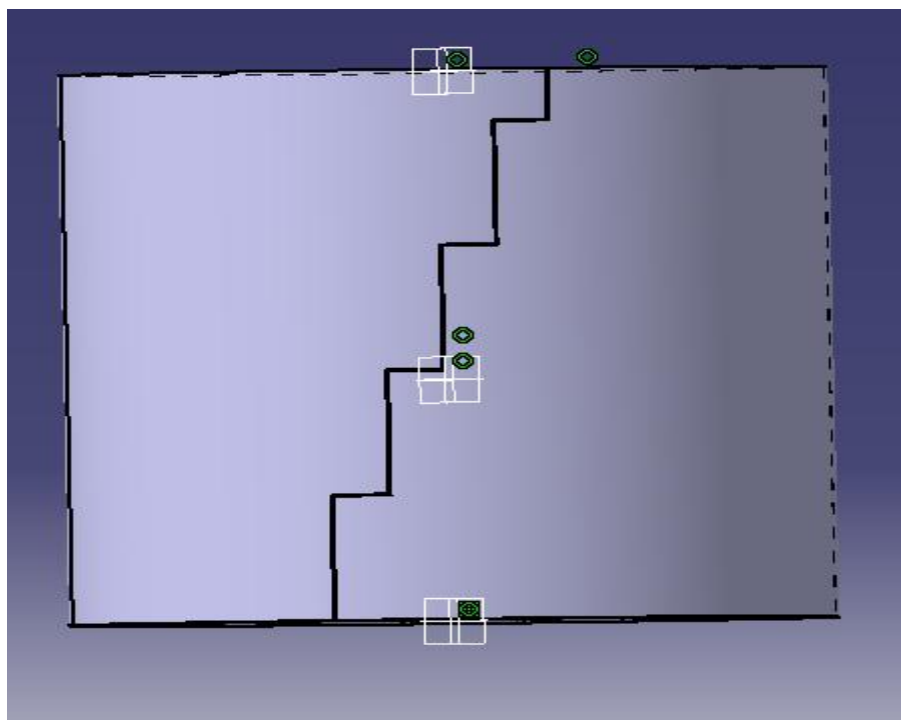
Просторова модель резервуару зі швом, як цільна деталь
